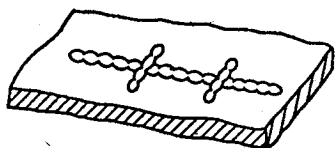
Схема установки уплотняющей и стягивающей вставок
